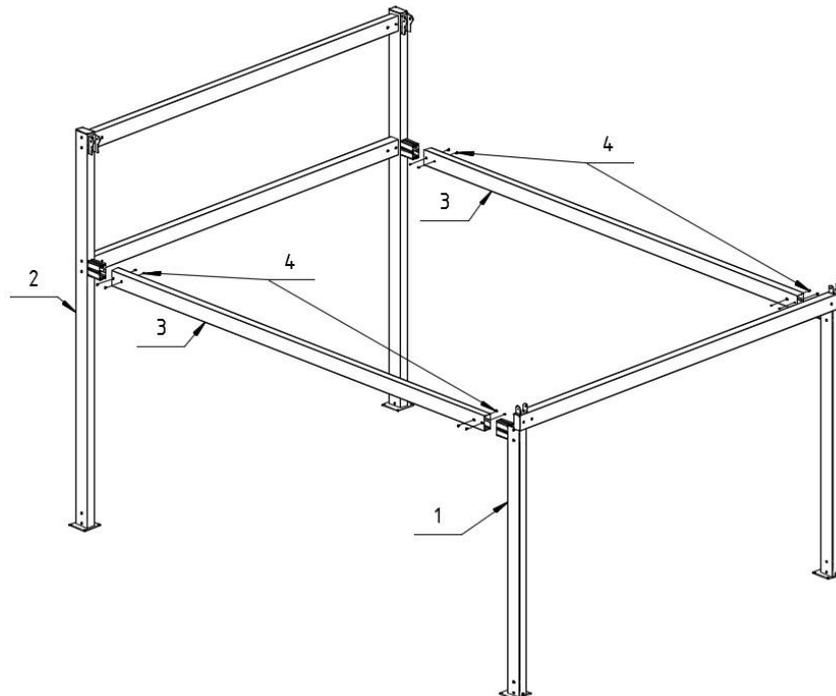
Manière de montage des barres latérales: 1 - Module du poteau bas, 2 - Module du poteau haut, 3 - Barre latérale, 4 - Vis M8x16.
